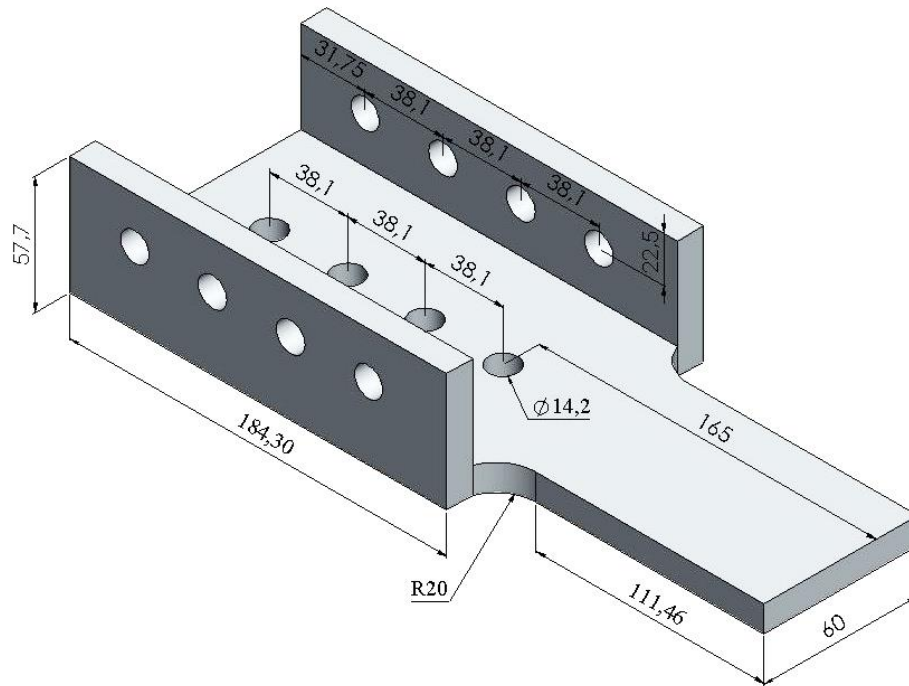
Dispositivo para fixação de perfis U com flanges de 45 mm de altura, dimensões em (mm)
